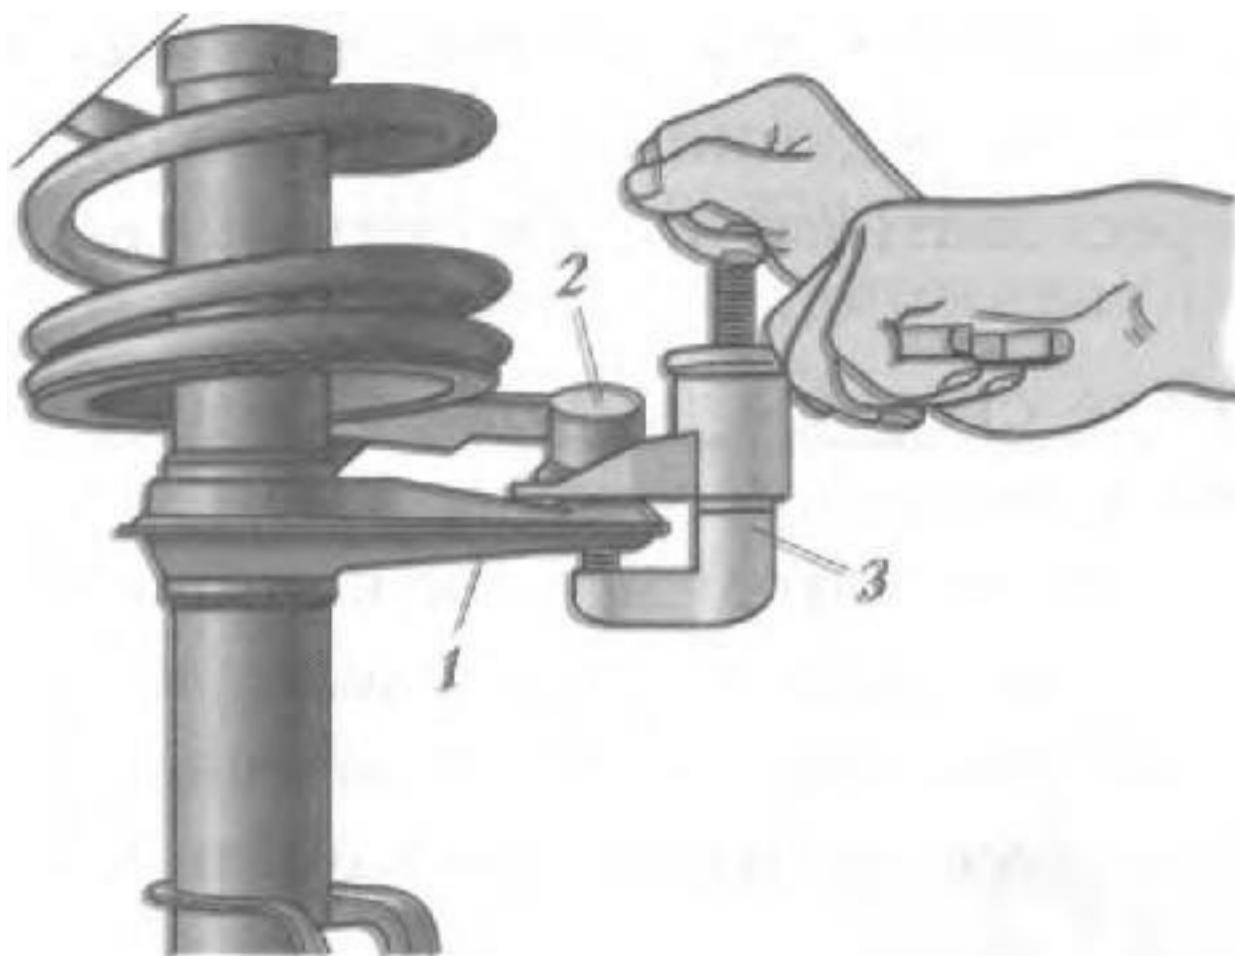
Выпрессовка пальца шарового шарнира рулевой тяги из поворотного рычага стойки подвески:
